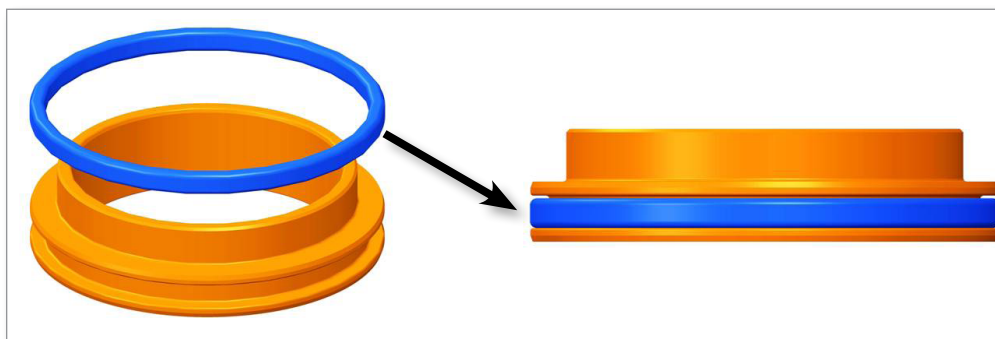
Installazione degli O-ring della parte inferiore del pistone
